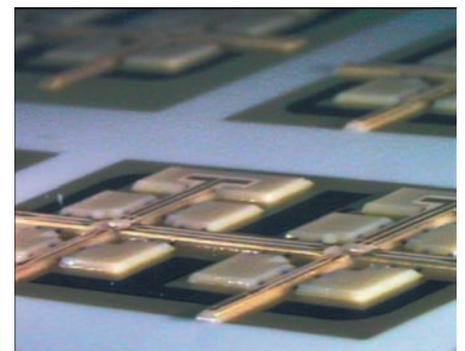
Фотография промежуточной стадии изготовления, показывающая несколько микросхем Quick Film
